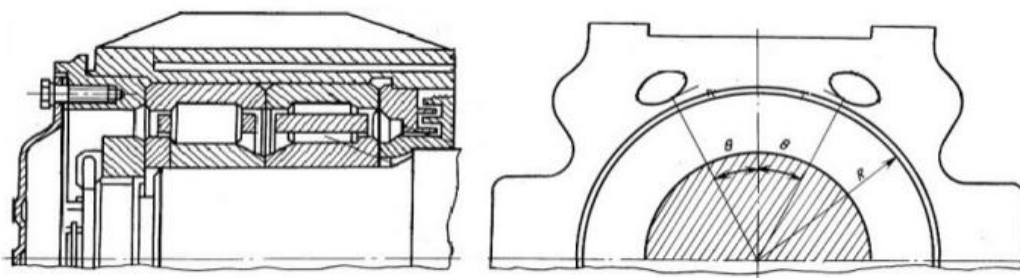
Буксовий вузол з прорізами у верхньому зводі корпусу
